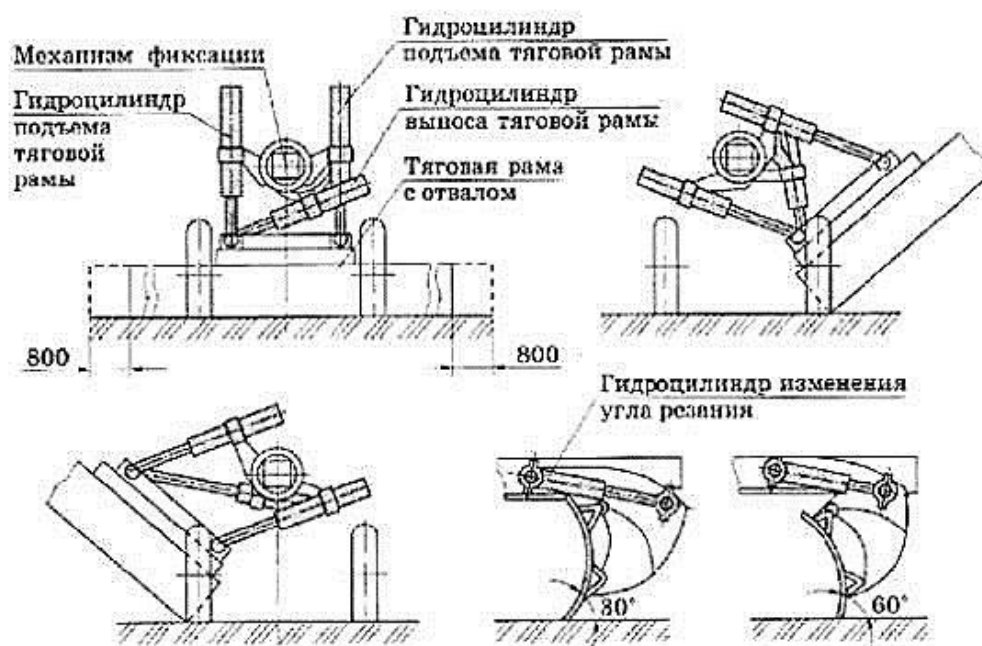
Схема рычагов и гидроцилиндров при различных положениях отвала
